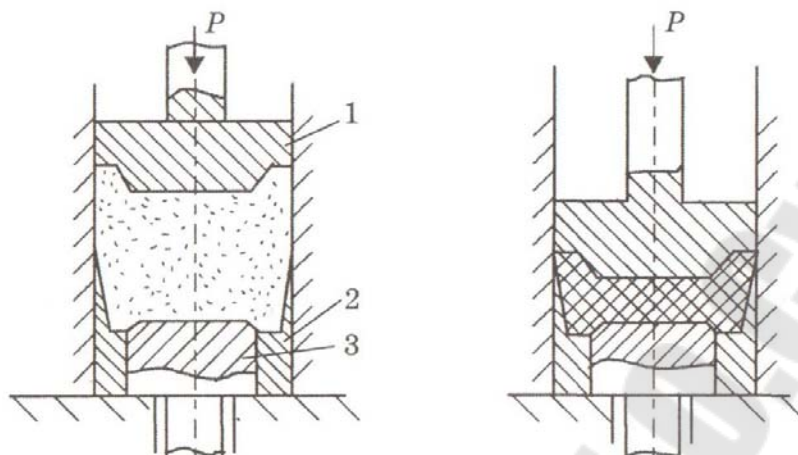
Схема изготовления детали методом прямого прессования:
